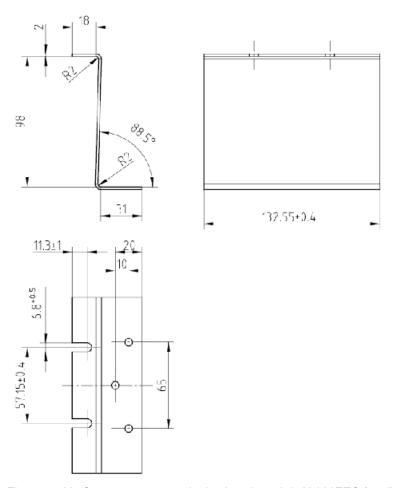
Soporte para montaje de pieza lateral de X-300EEC (medidas en mm)
